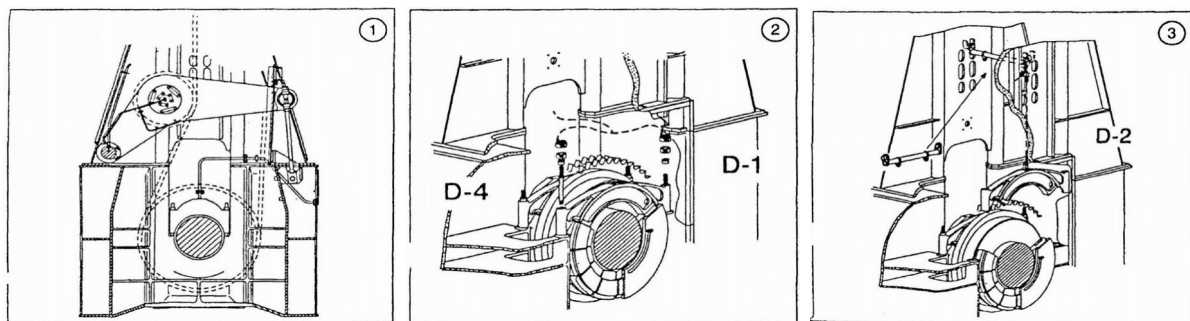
Підготовка до розбирання упорного підшипника
